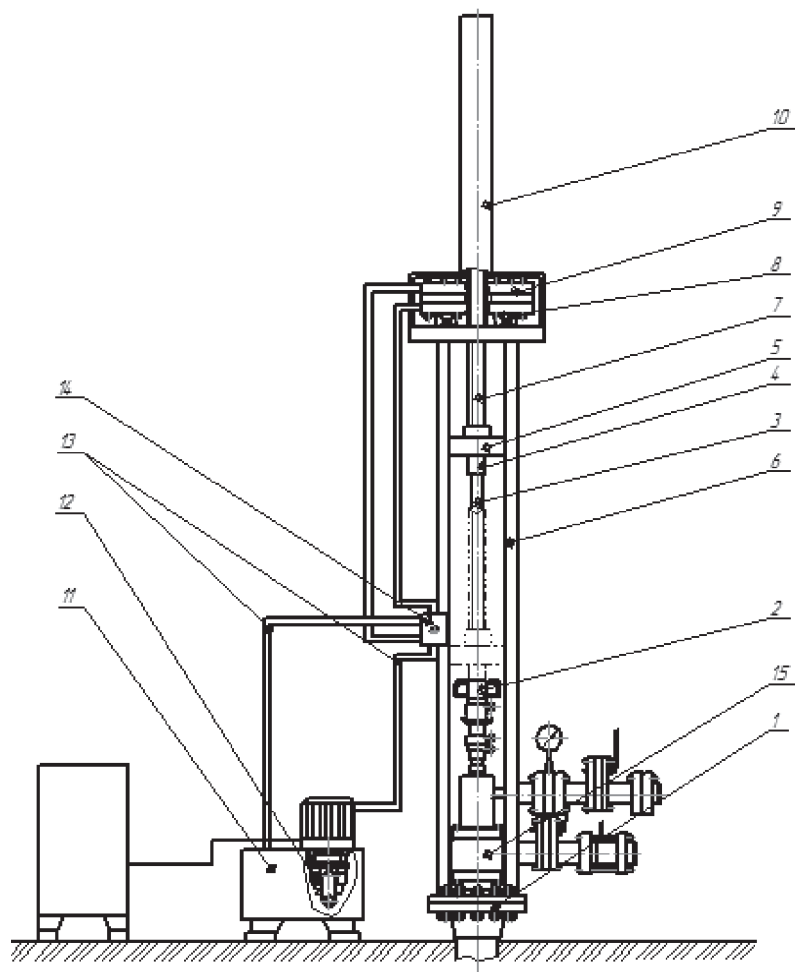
Гидровинтовой привод ШСН: 1 – фланец колонной обвязки; 2 – устьевой сальник; 3 – полированный шток; 4 – узел подвески; 5 – каретка; 6 – корпус; 7 – приводной винт; 8 – подшипники; 9 – гидродвигатель; 10 – защитный кожух; 11 – гидробак; 12 – силовой насос; 13 – маслопроводы; 14 – гидрореле; 15 – малогабаритная устьевая арматура
